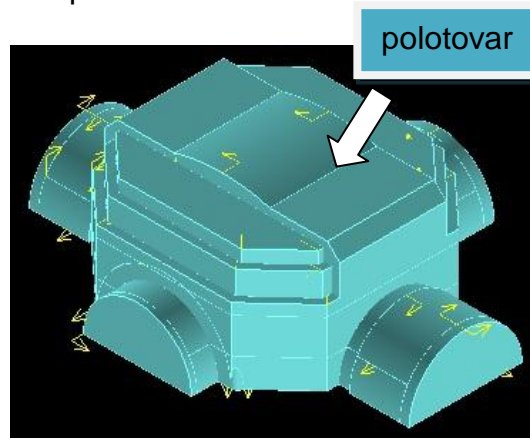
Zobrazení načtené geometrie modelu vršek a barva hladiny a souřadného systému
